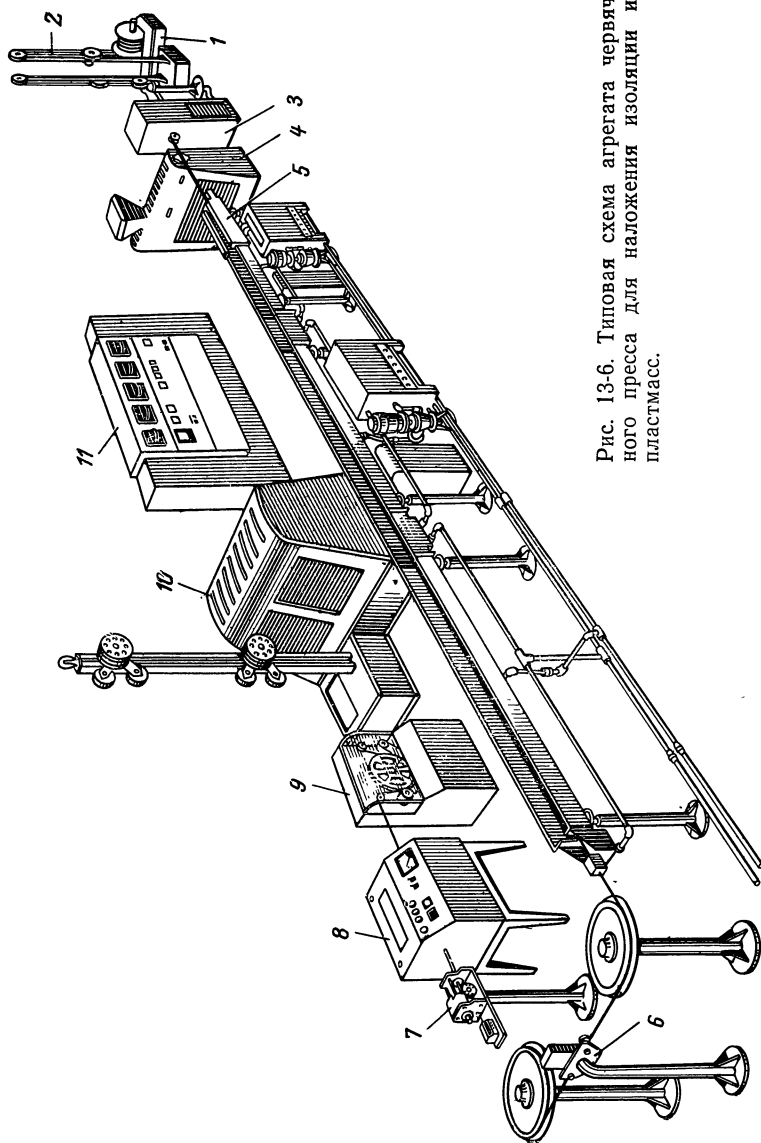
Типовая схема агрегата червячного пресса для наложения изоляции из пластмасс.
